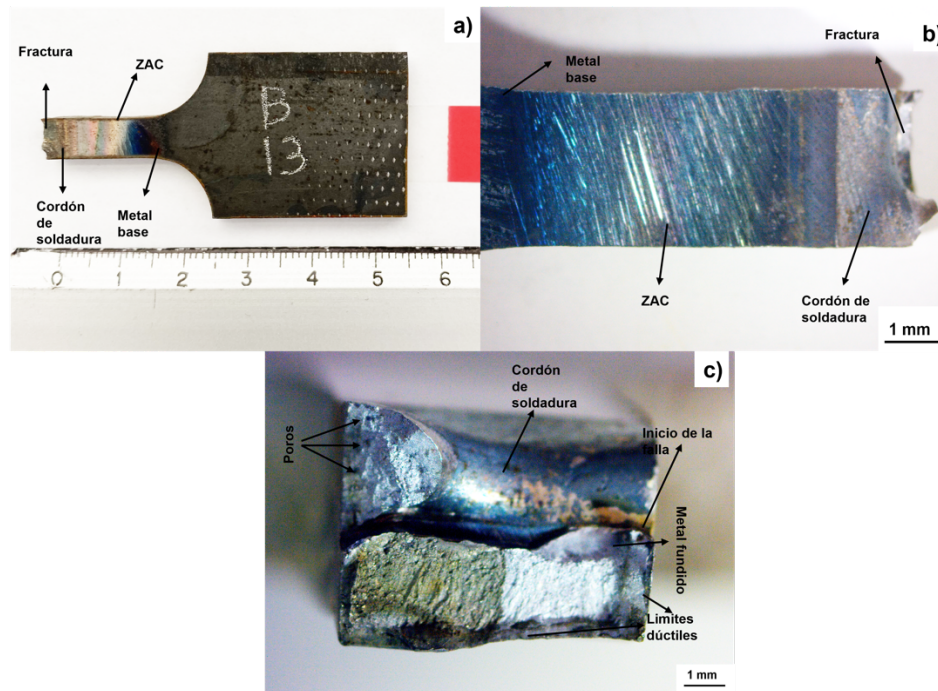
Estereoscopia de unión GTAW13 donde a) en vista macroscópica se observa la mitad de unión con fractura en el cordón de soldadura, b) a 6.5 x se muestra en vista longitudinal la ZAC y la fractura en el cordón, c) en vista transversal se muestra falta de penetración con grieta en el cordón
